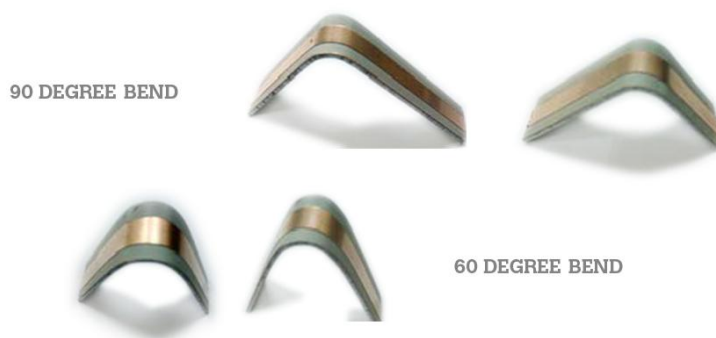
варіанти вигнутих плат із металевою основою MC PCB компанії BAKNOR
